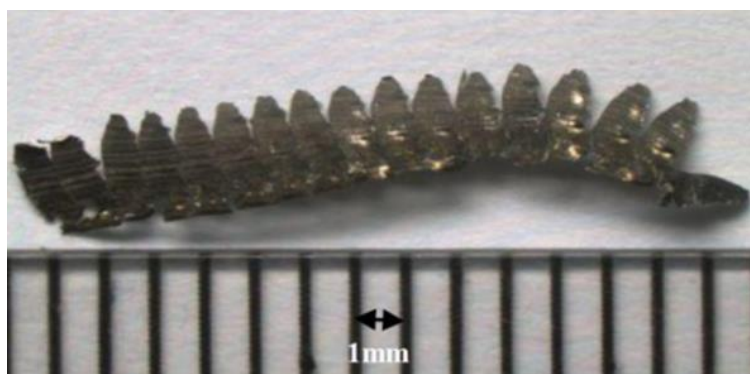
Cavaco serrilhado obtido por usinagem de material Inconel 718, com fresa de topo esférico em estratégia de corte concordante [21]
